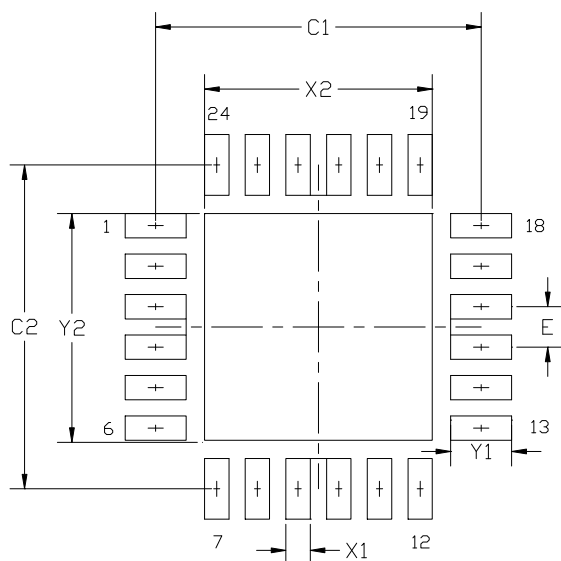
QFN-24 建议的 PCB 焊盘图案
